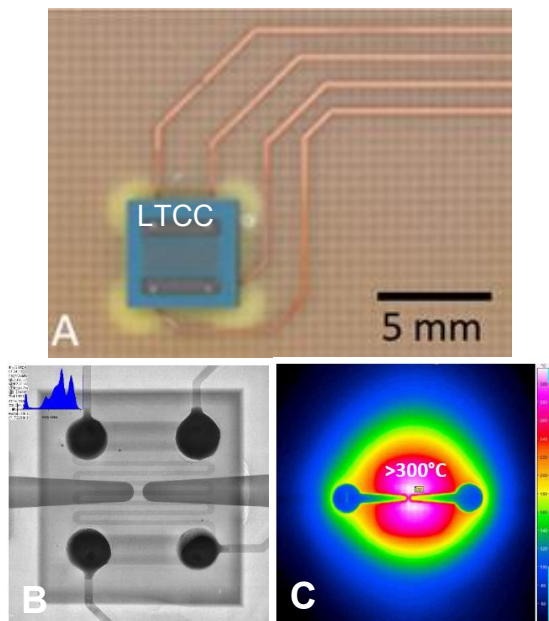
Draufsicht auf Heizelement integriert in PCB (A), zugehörige Röntgenmikroskopie- (B) und Thermografie-Aufnahme (C)
